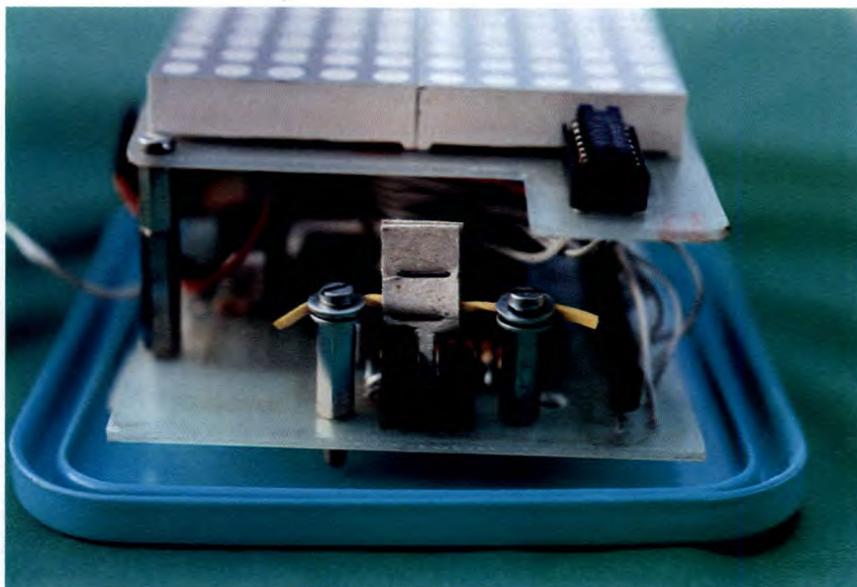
Disposizione dei componenti sulla basetta principale.
